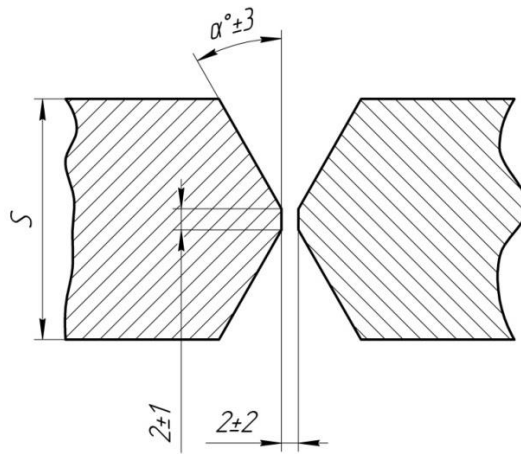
Стыковое сварное соединение с двумя симметричными скосами кромок типа С25
